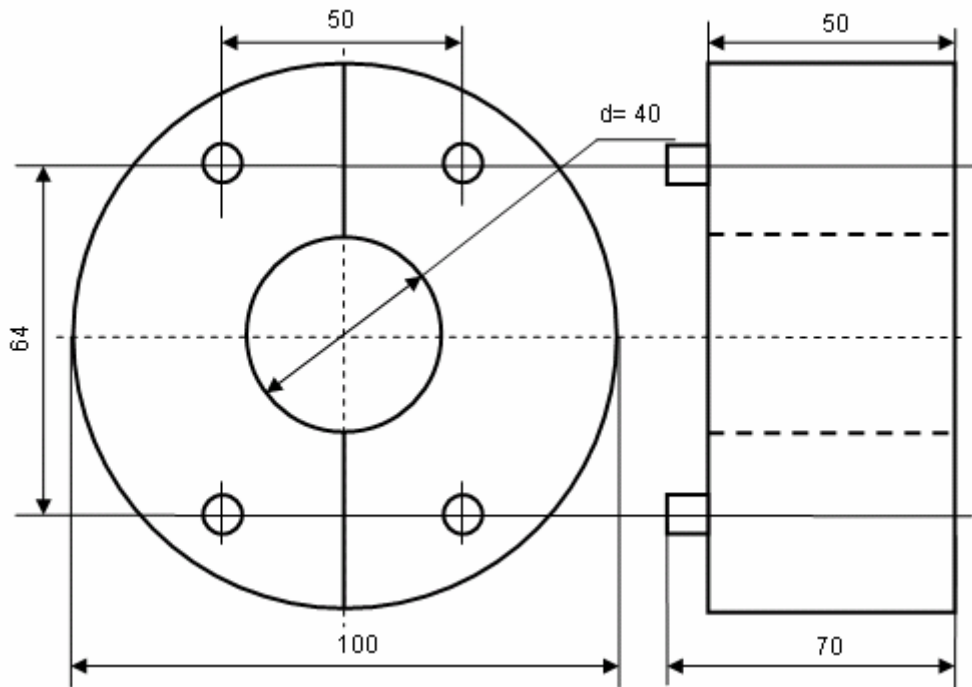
Габаритные размеры воздушного трансформатора тока
